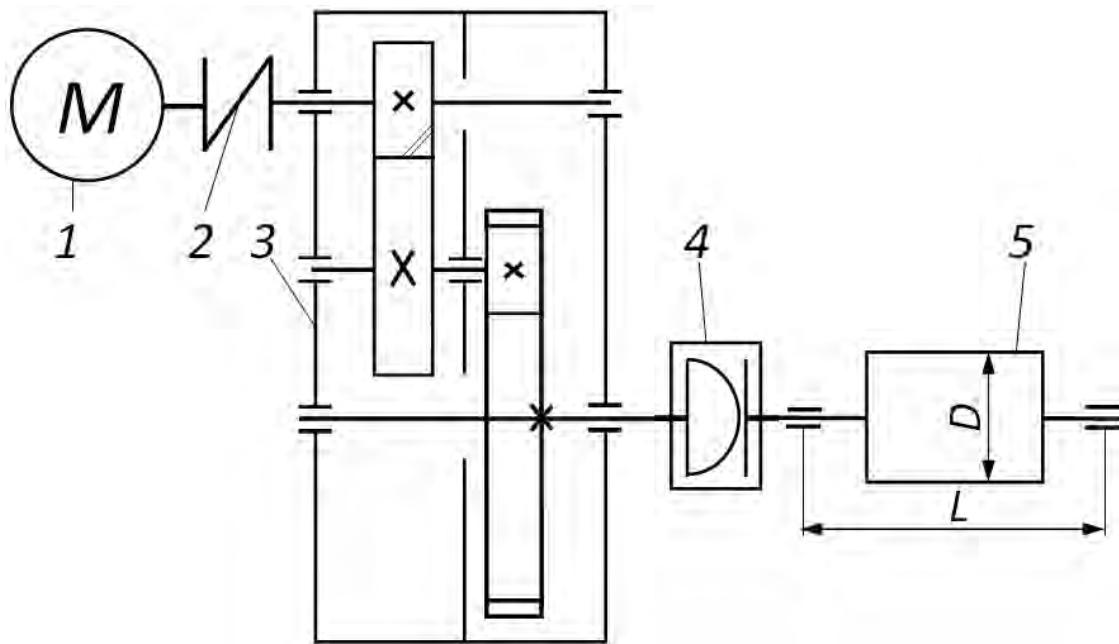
Схема привода ленточного конвейера (вид сверху): 1 – асинхронный электродвигатель; 2 – муфта упругая втулочно-пальцевая; 3 – редуктор цилиндрический двухступенчатый (первая ступень – цилиндрическая косозубая зубчатая передача, вторая – цилиндрическая прямозубая зубчатая передача с внутренним зацеплением); 4 – муфта кулачково-дисковая; 5 – приводной вал с барабаном
